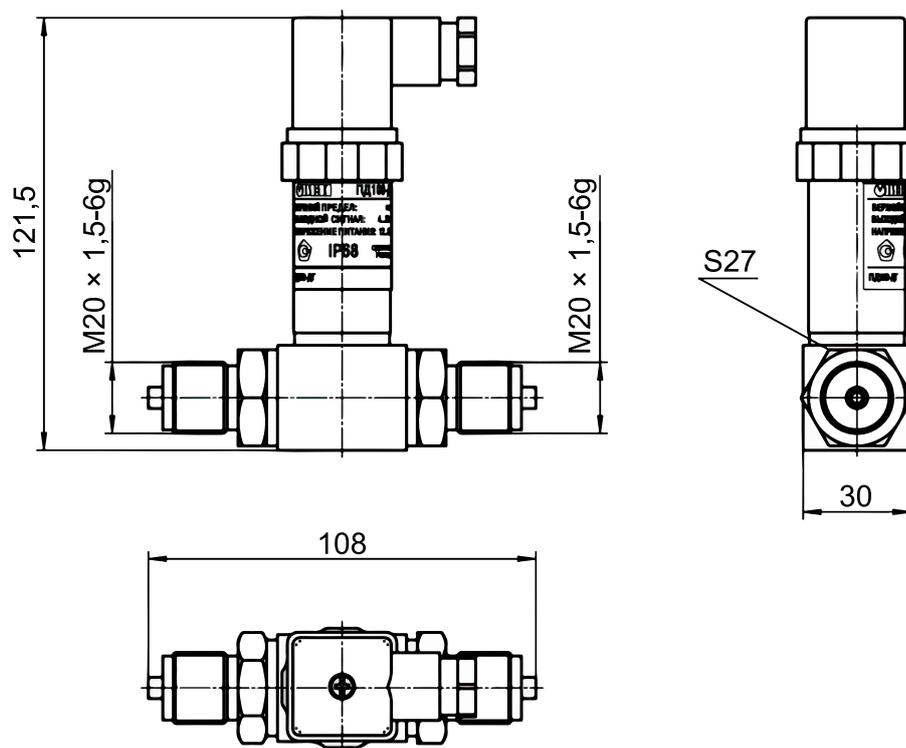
Габаритные и присоединительные размеры преобразователей ПД100-ДД
